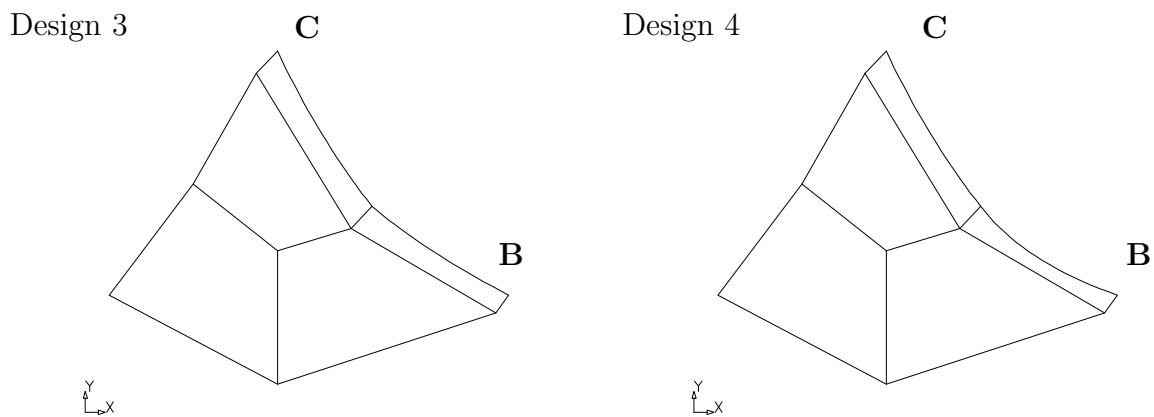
Ausbildung der Schweißnaht für das Design 3 und 4
